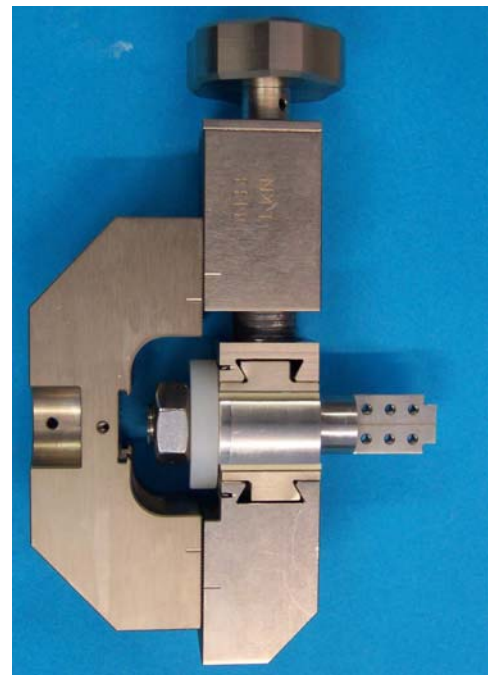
Befestigung des Probenhalters im Zwick8133 Halter
